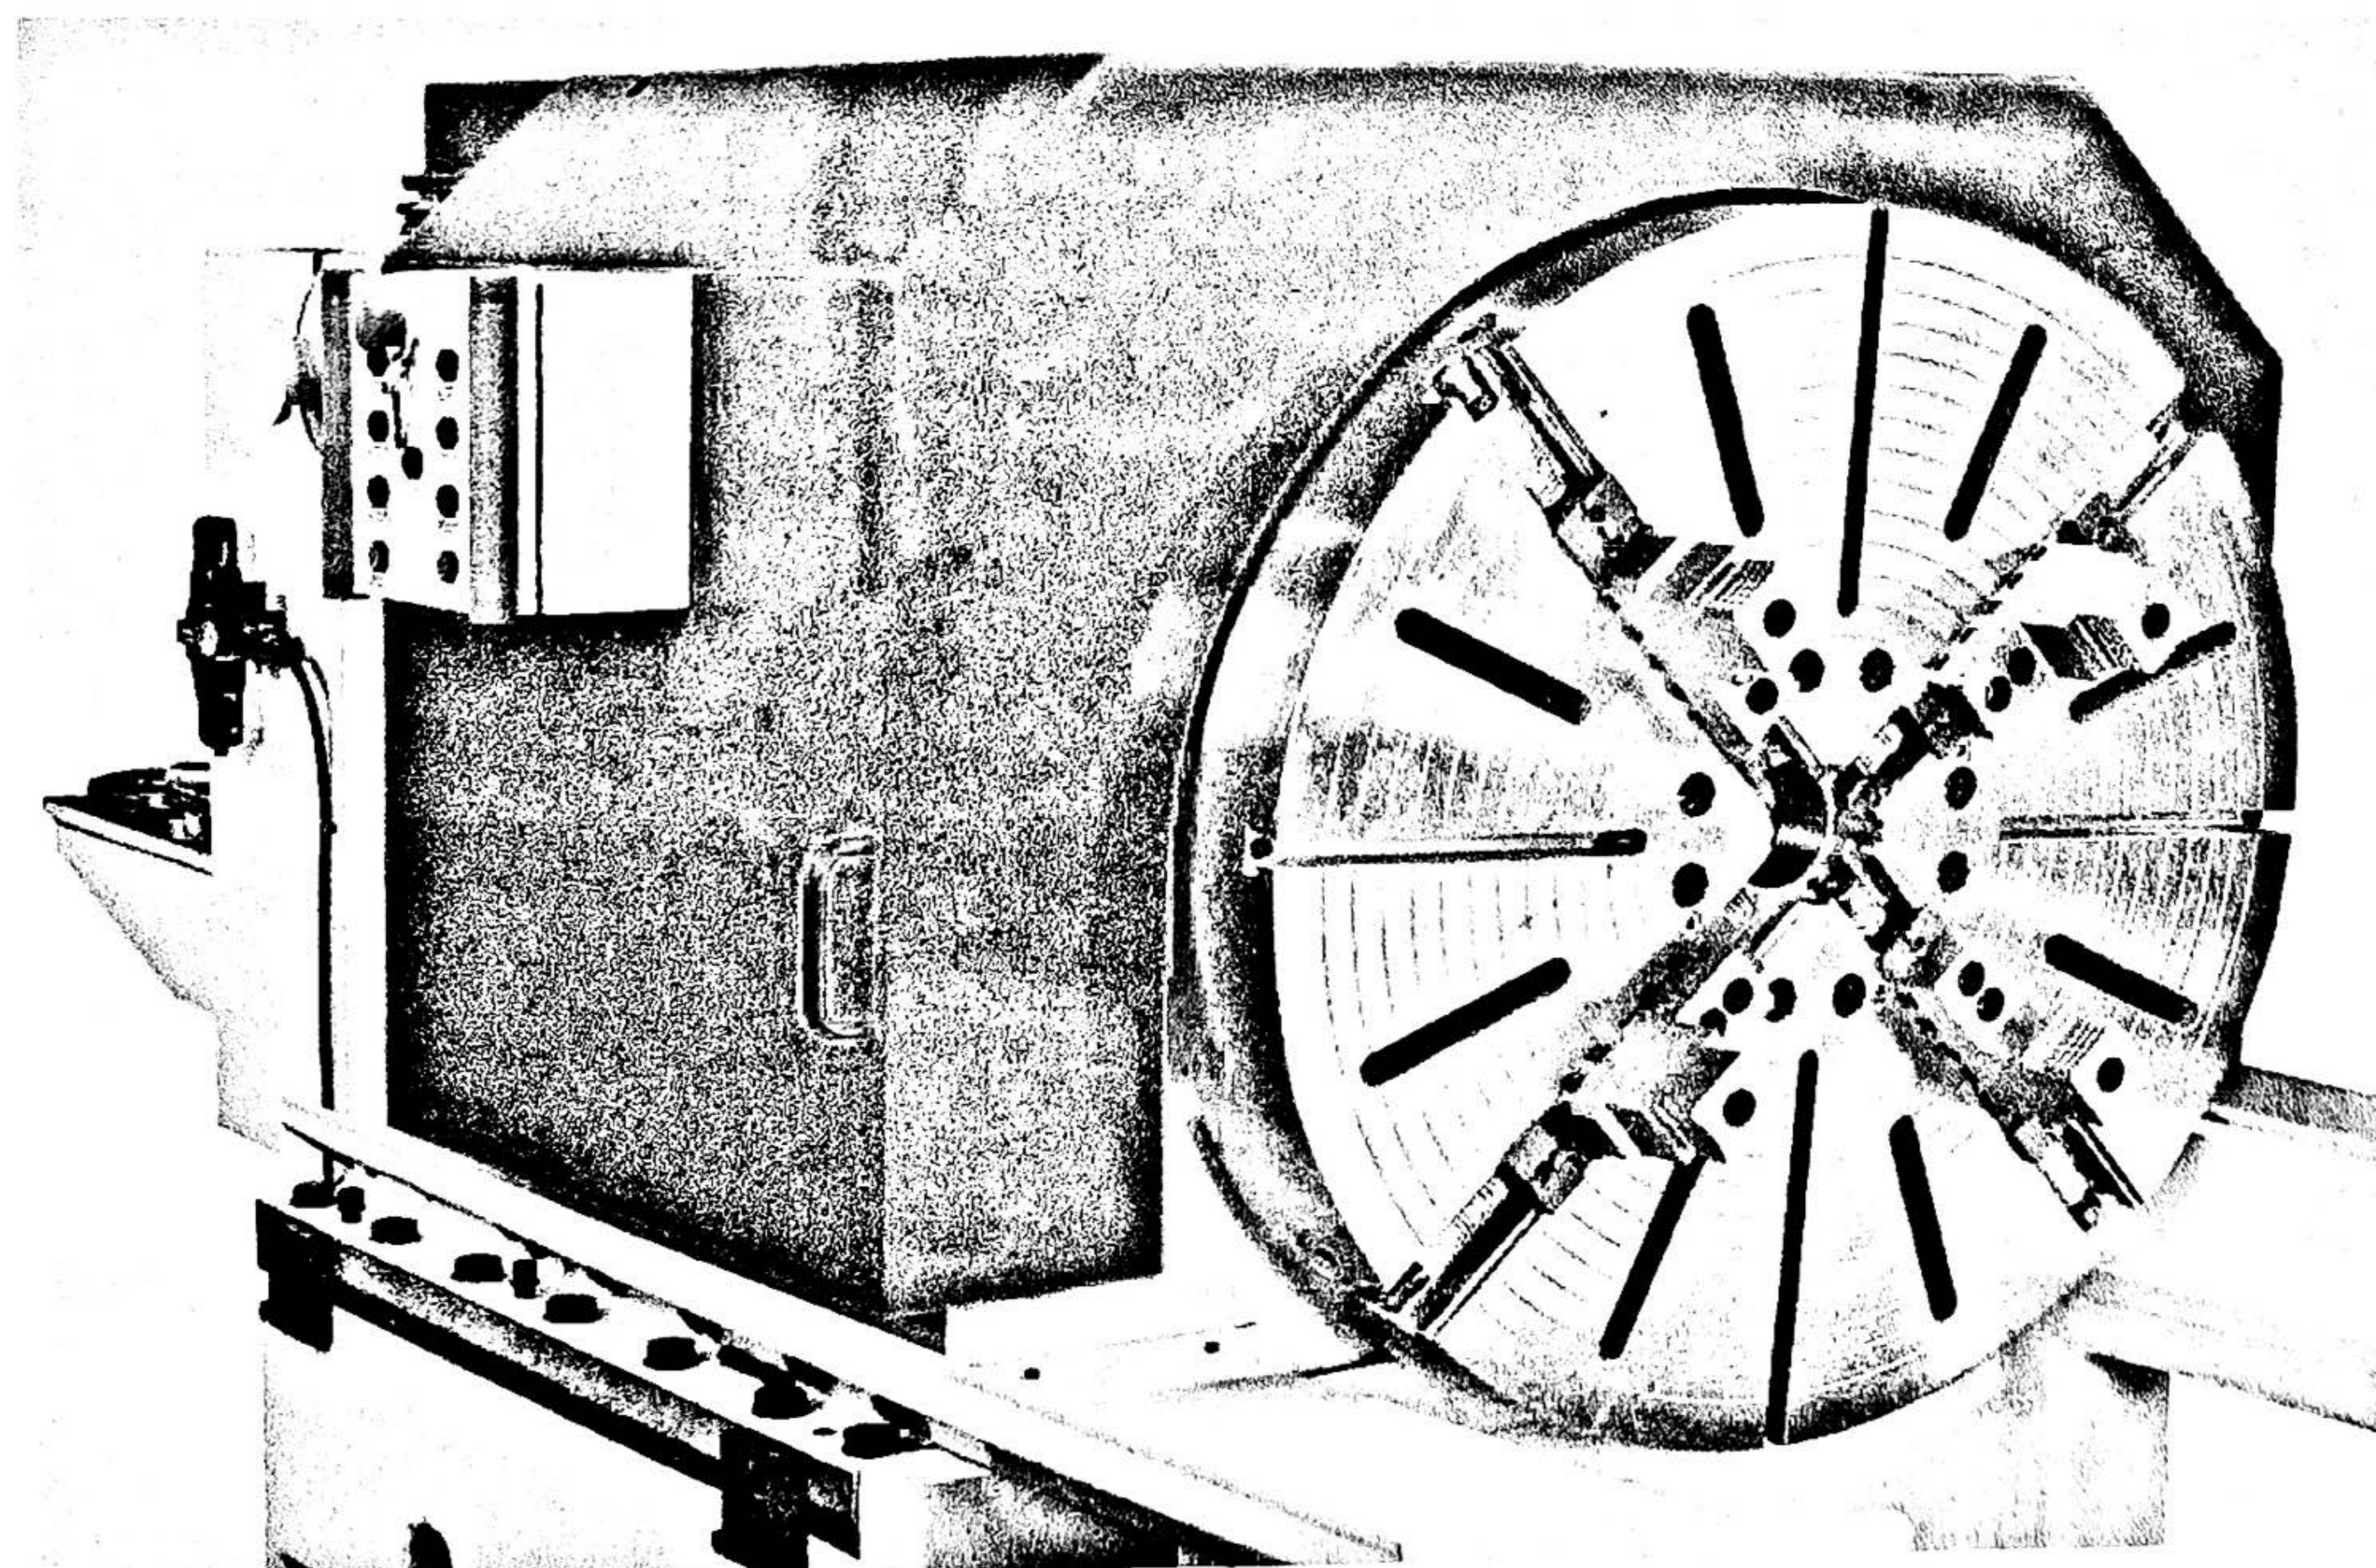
/6: Spindelkasten mit Schutzhaube (geöffnet) und Nebenbedienpult (E6)
